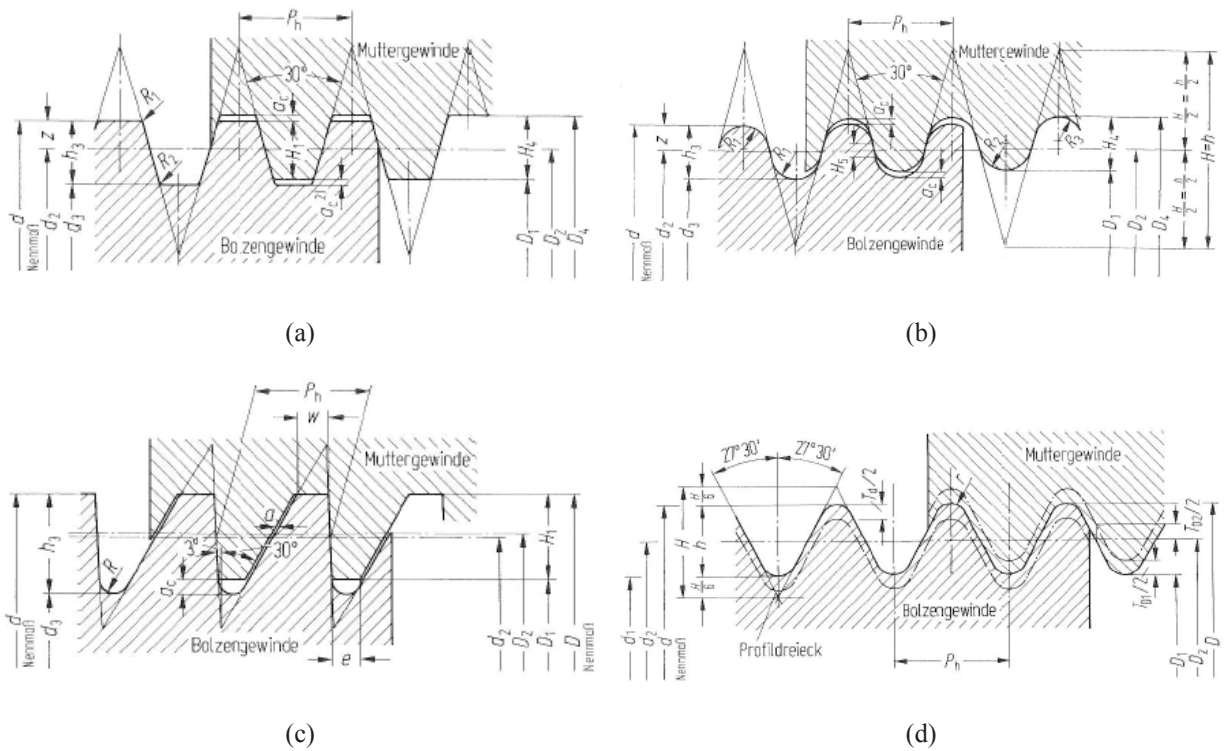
(a) Trapezgewinde DIN 103 (b) Rundgewinde DIN 405 (c) Sägezahnengewinde DIN 513 und (d) Withworthgewinde [6]
